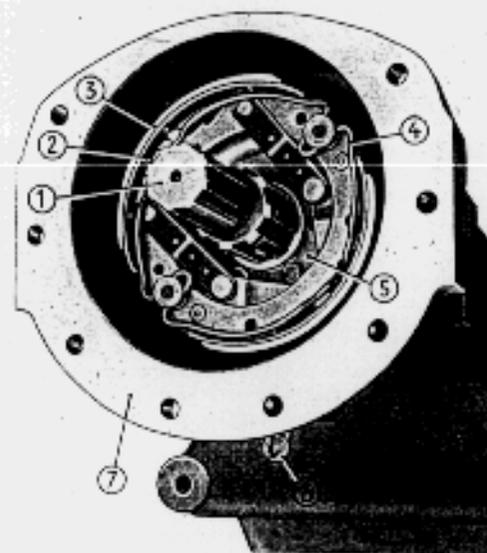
Bremse (Achsröhre abgebaut, Bremsstrommel ausgebaut)
